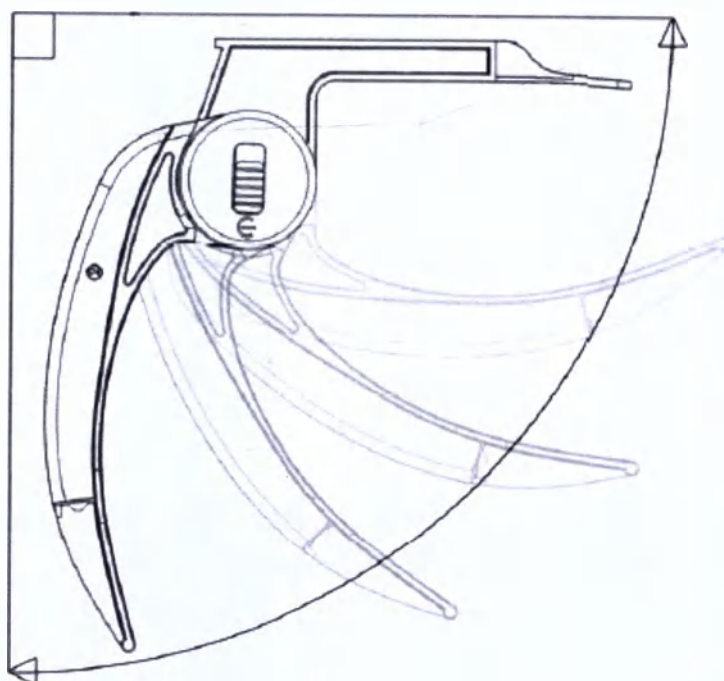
смеха поворота двойного клинка для подготовки к использованию
